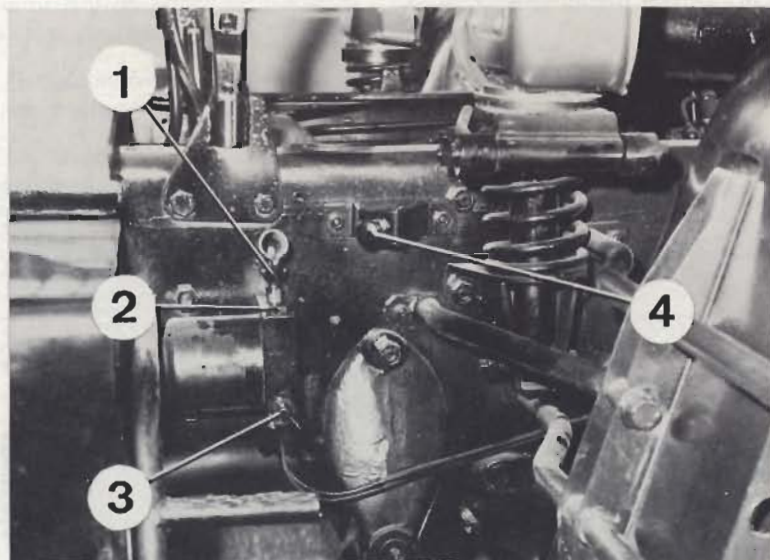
Bomba hidráulica elevación cabina y paro-motor
